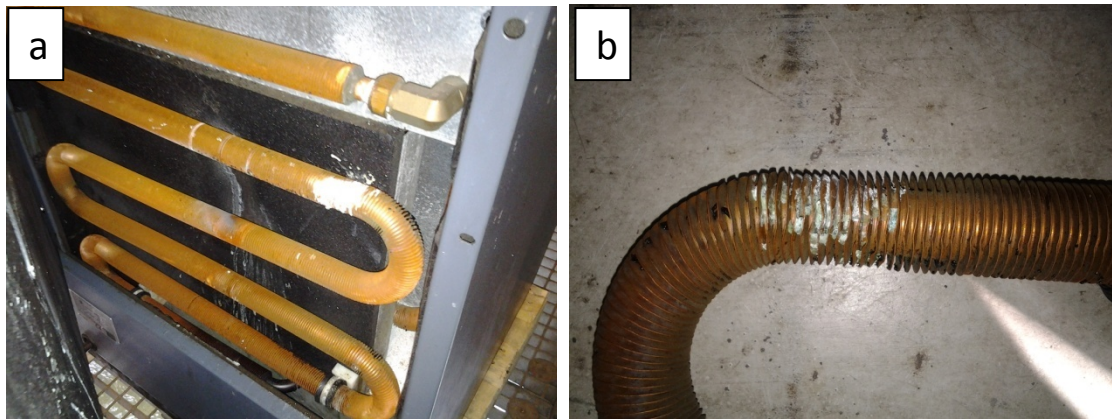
a) Rauchgaskompressor mit Blick auf die Hinterseite, Ausführung Scrollkompressor, ölfrei. Die hellen Stellen zeigen durch die schweflige Säure durchgeätzte Leitungen. b) Detailansicht
